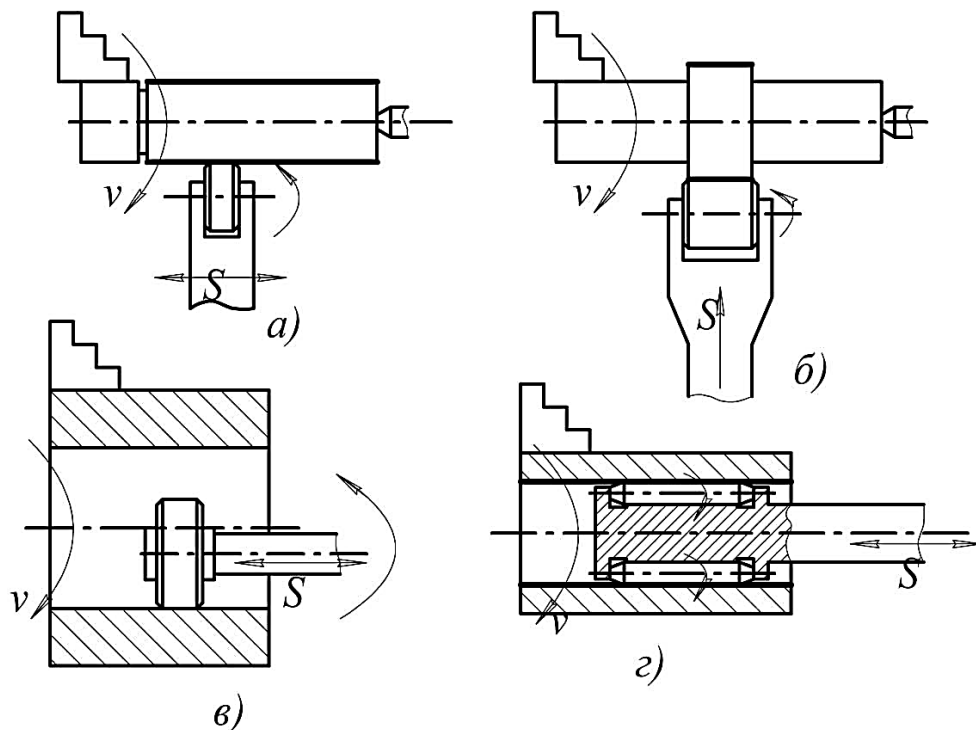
Схеми накатування і розкатування поверхонь
